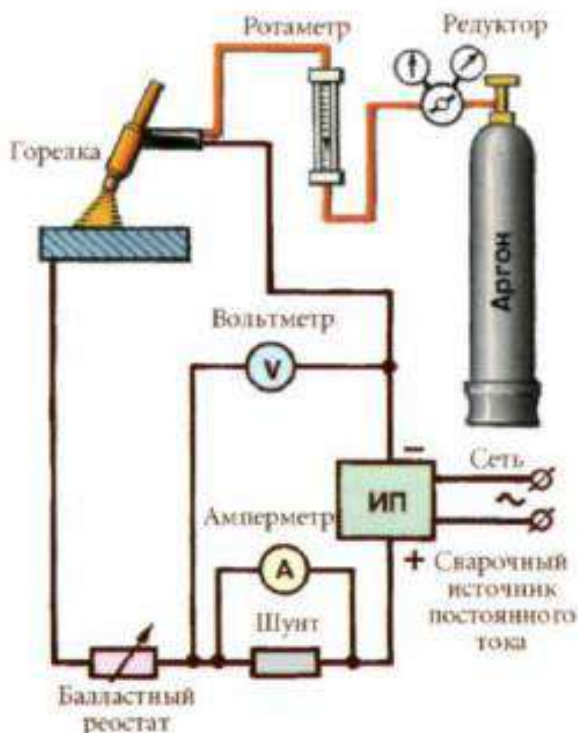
Схема оборудования для сварки на постоянном токе.
